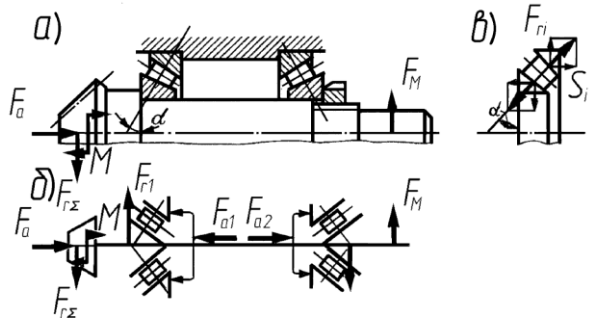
17. Конструктивна (а) і розрахункова (б) схеми для підшипників вала конічної шестерні
